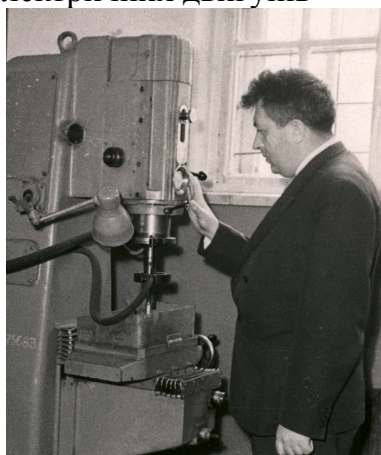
Старший викладач кафедри О.А. Коломойцев налагоджує електроерозійний верстат, призначений для виготовлення отворів у твердосплавних деталях
